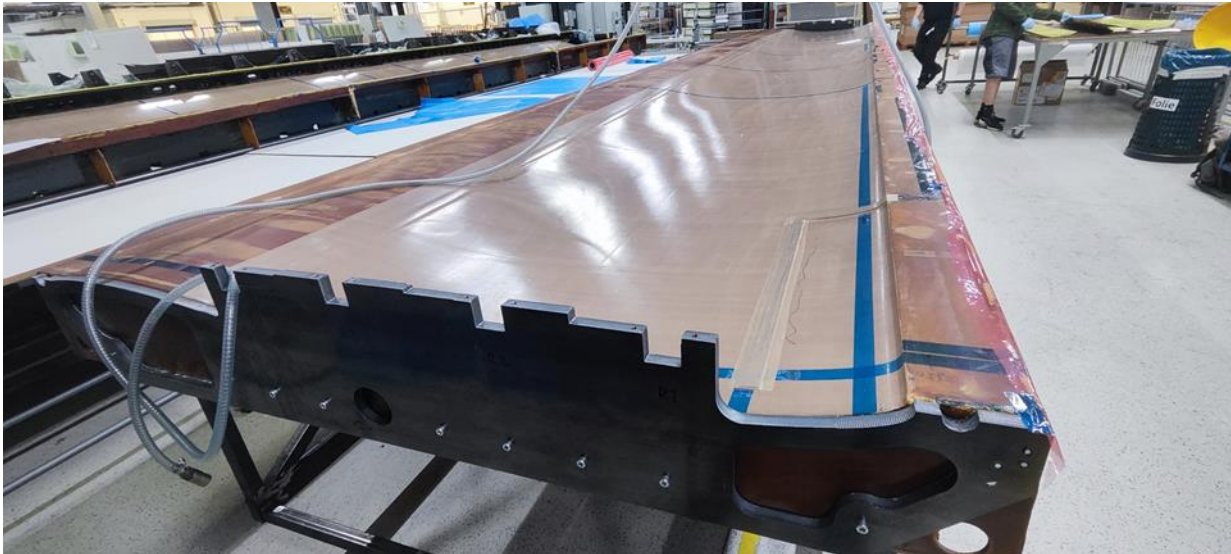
Positionierungshilfe im Formwerkzeug UFS
